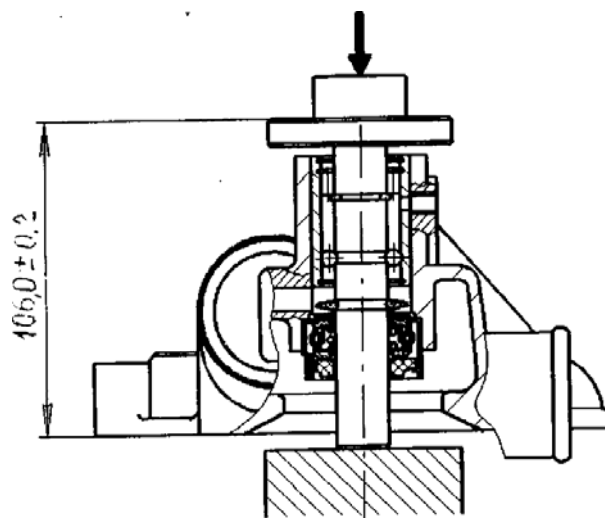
Напрессовка ступицы шкива водяного насоса на вал
